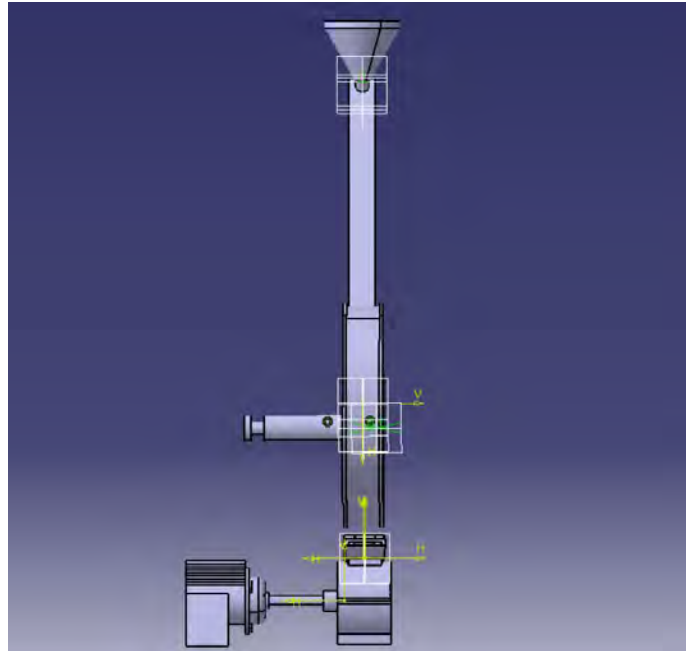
Vista frontal del ensamble de la máquina de descascarado (realizado en Catia V5)
